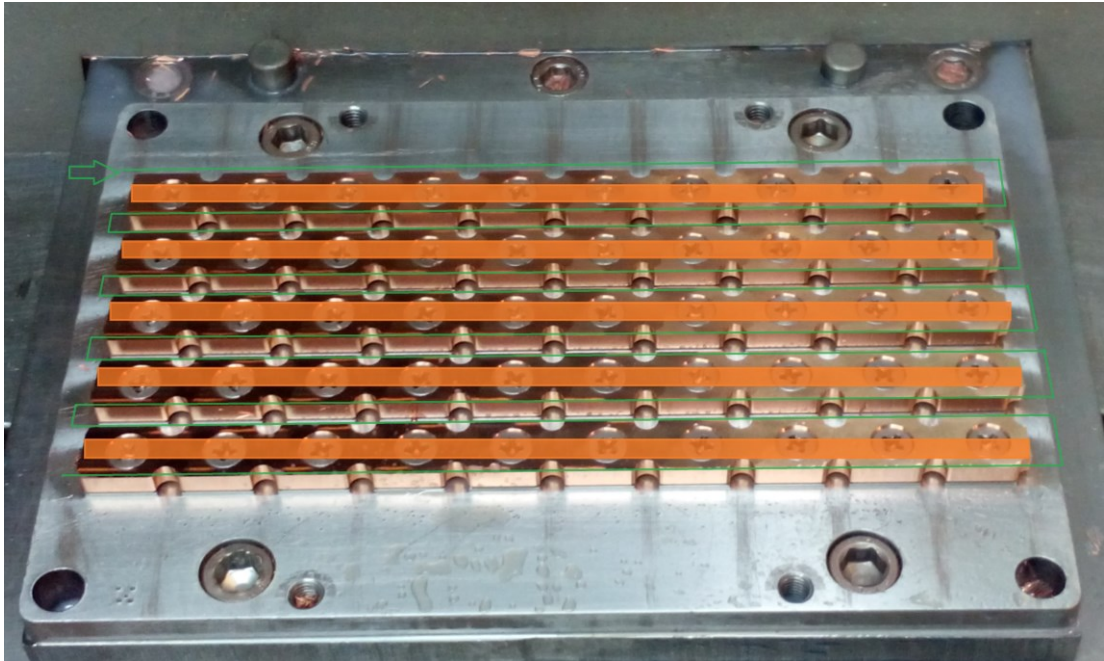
Připevněné pásky připravené k 1. programu frézování
